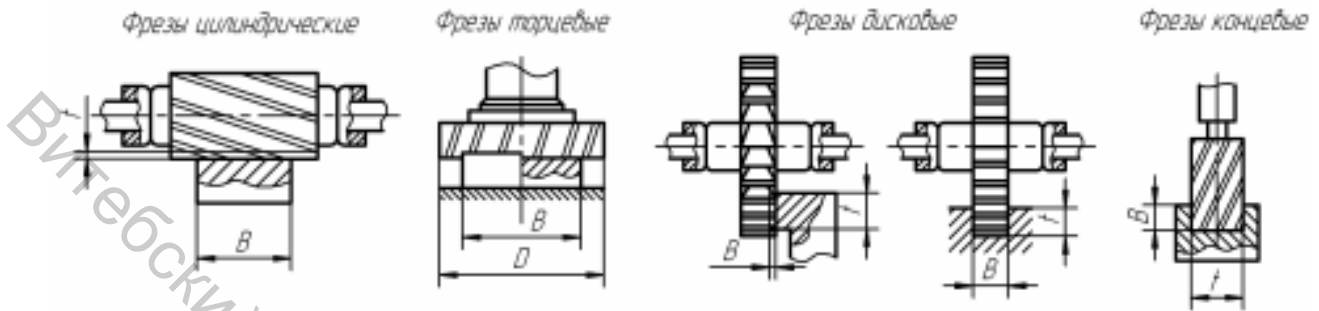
Основные виды фрезерования: D – диаметр фрезы; B – ширина фрезерования; t – глубина фрезерования
